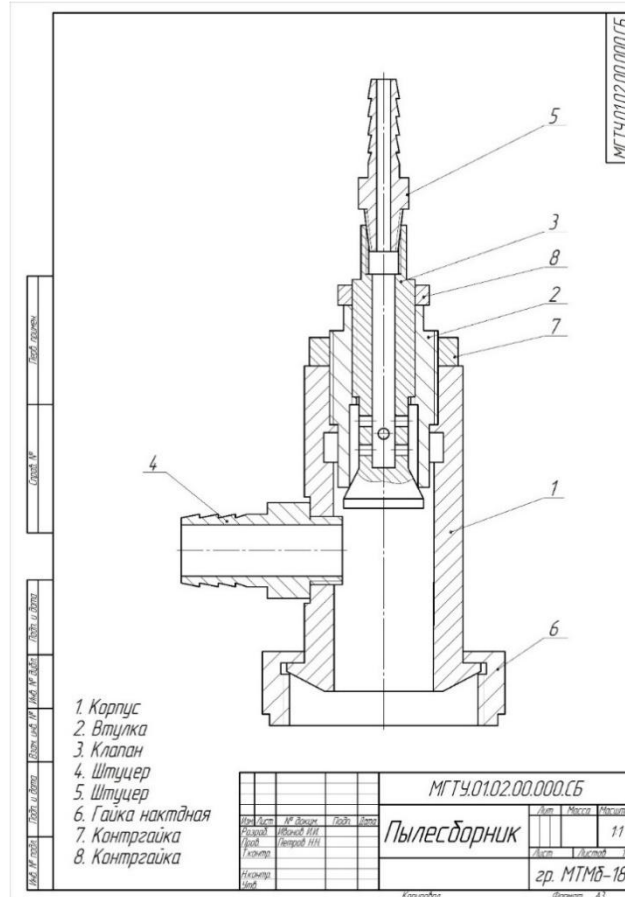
Сборочный чертеж пылесборника инжекторного, используемый в качестве метки для AR-приложения
